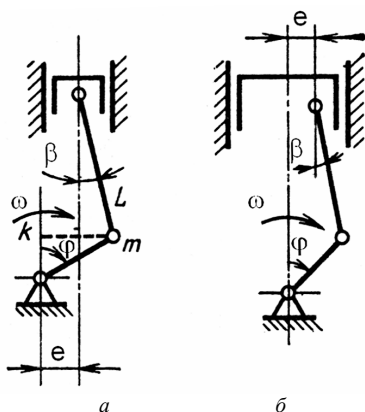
Дезаксиальный кривошипно-шатунный механизм: a – со смещением оси коленчатого вала; b – со смещением оси верхней головки
